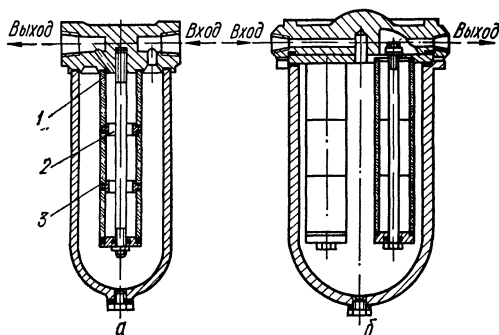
Типовые (ГОСТ 12455—72) конструкции металлокерамических фильтров: *a* — с несколькими фильтроэлементами и мягкими прокладками; *b* — с фильтроэлементами, соединенными аргоно-дуговой сваркой; 1 — фильтроэлемент; 2 — промежуточное кольцо; 3 — прокладка.
